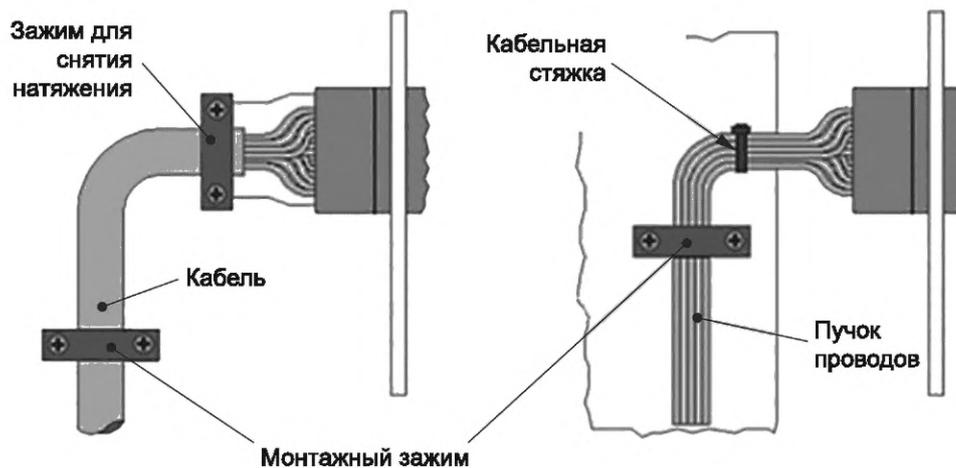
Монтаж жгутов проводов/кабелей с подключением к СПИ
